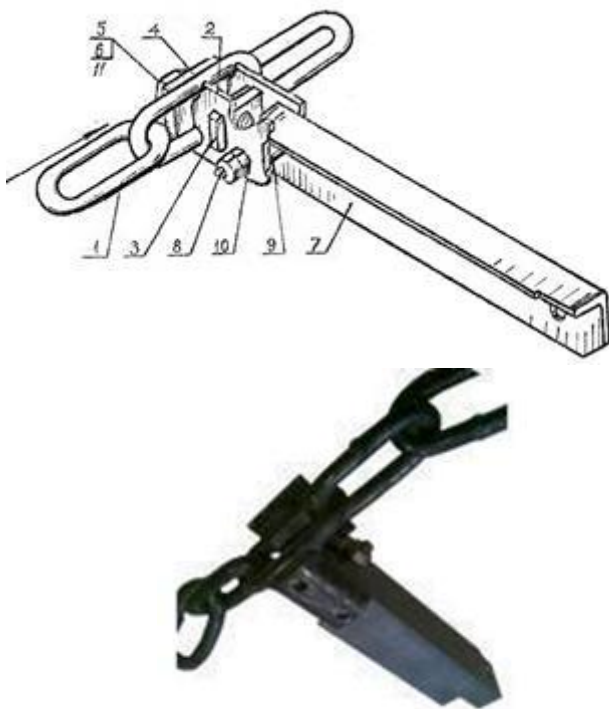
Кріплення скребка конвеєра КСГ-7: 1 – ланцюг; 2 – основа; 3 – пластина; 4 – притискач; 5, 8 – болти; 6 – шайба; 7 – скребок; 9 – втулка; 10,11 – гайка.
